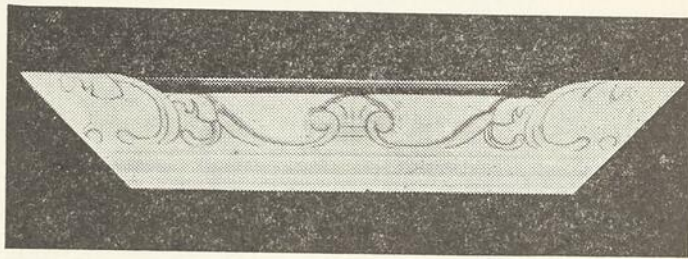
Le dessin est reproduit sur la moulure après que celle-ci a été coupée aux dimensions voulues.
